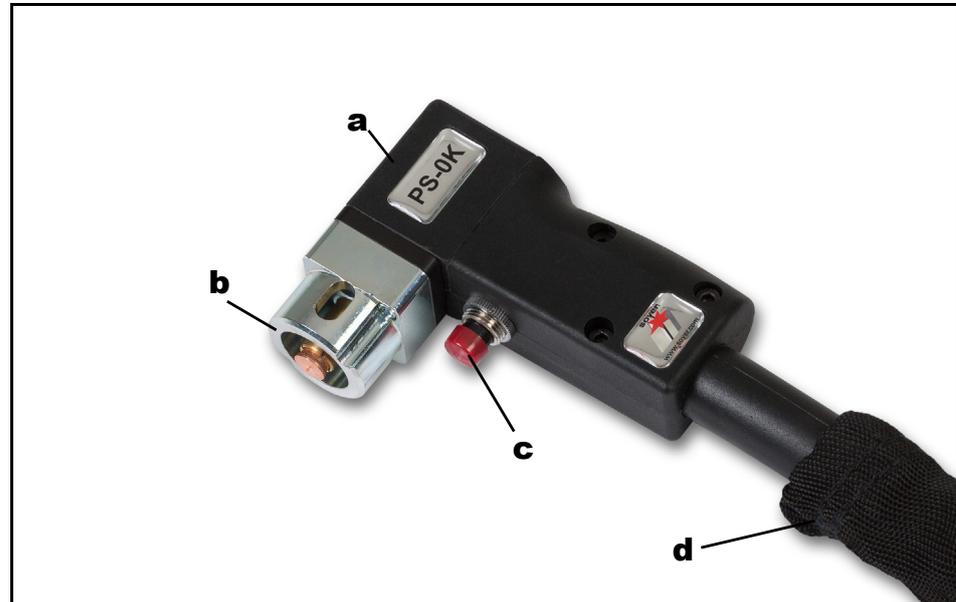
Bolzenschweißpistole PS-0K
